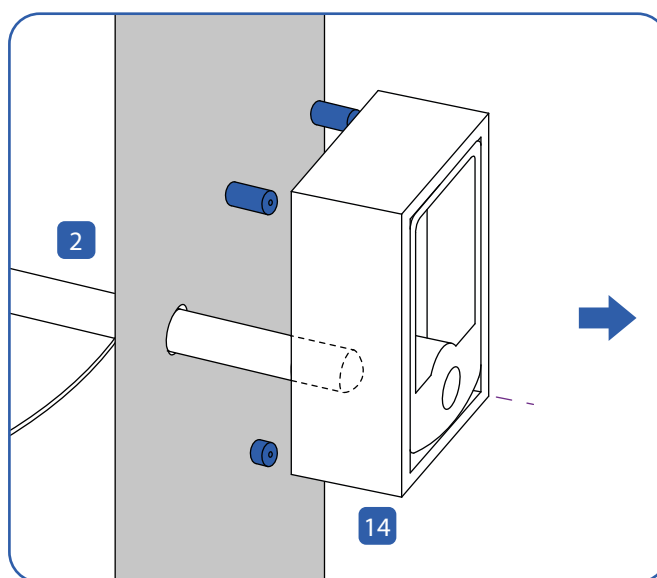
Ejemplo de montaje de una válvula VRC con su motor
